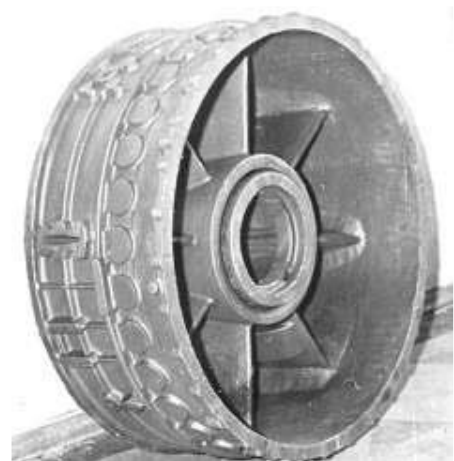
Корпус передньої опори зі сплаву МЛ9
